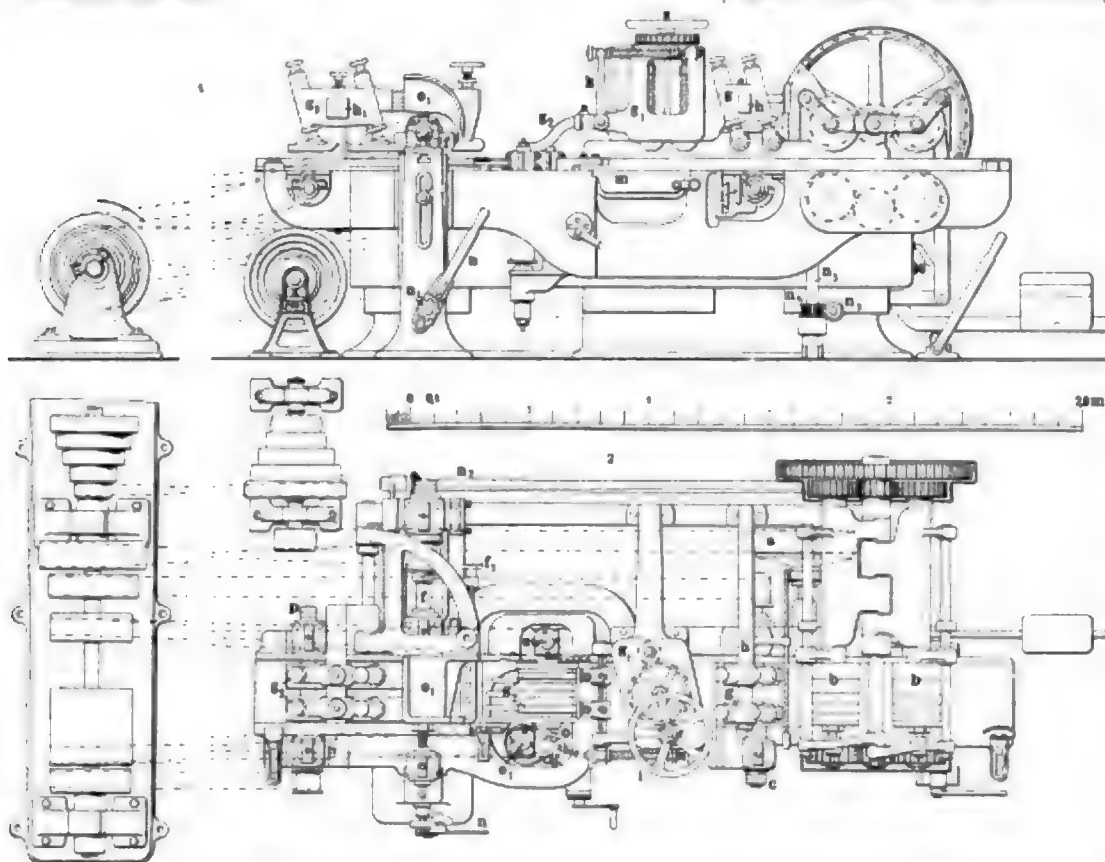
Vierseitige Wassenhobel-, Nut-, Spindel- und Kälmaschine von Gebr. Schmalz in Offenbach a. M.
